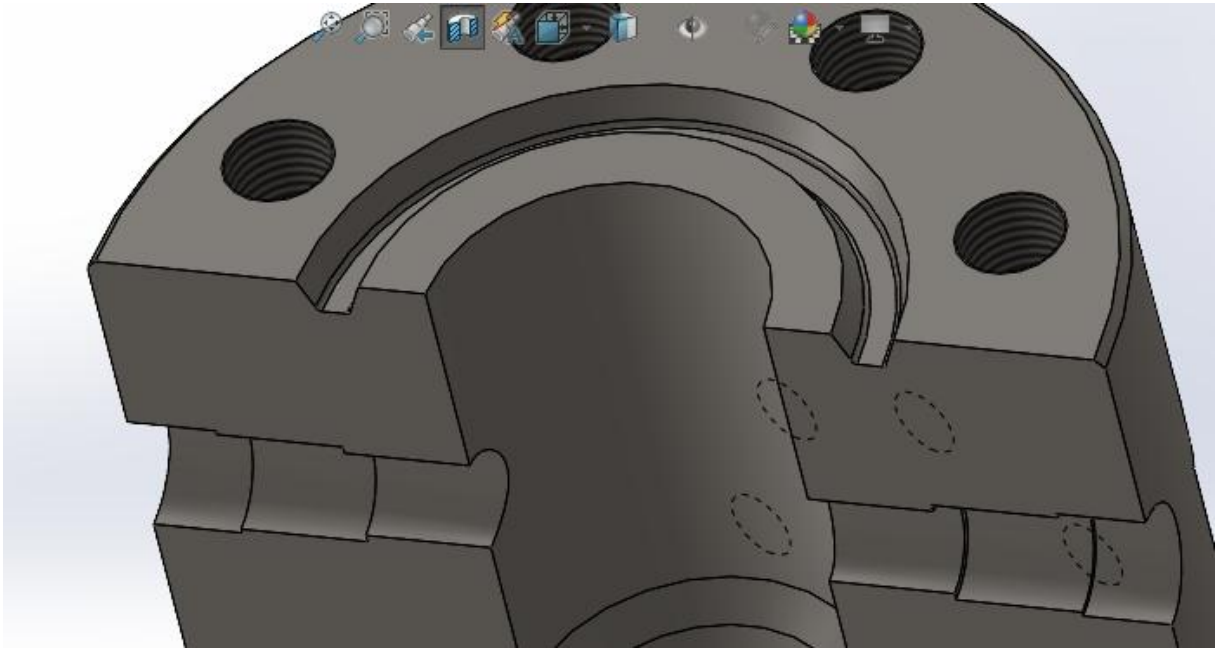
Vue en coupe 3D des trous de passage des pointeaux
